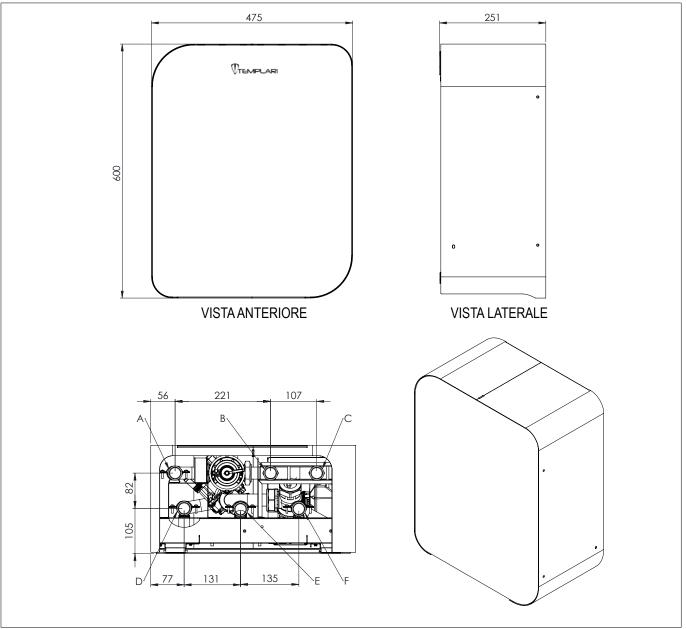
(Dimensioni versione senza touch e vista inferiore)
